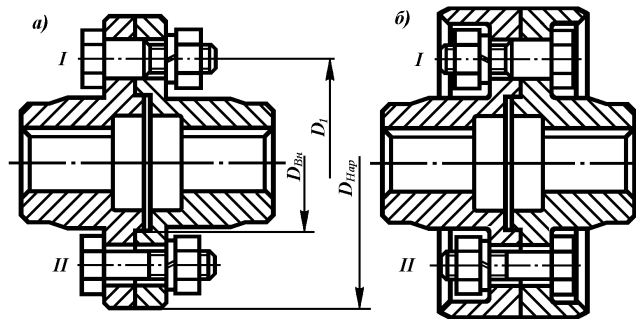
Муфта фланцевая: а) для закрытой установки; б) для открытой установки; I – призонные болты; II – обычные болты в отверстиях с зазором.
